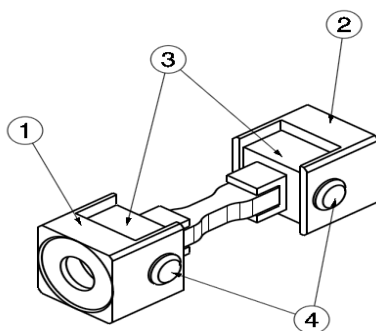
Aufnahmevorrichtung für PMI - Zugproben
